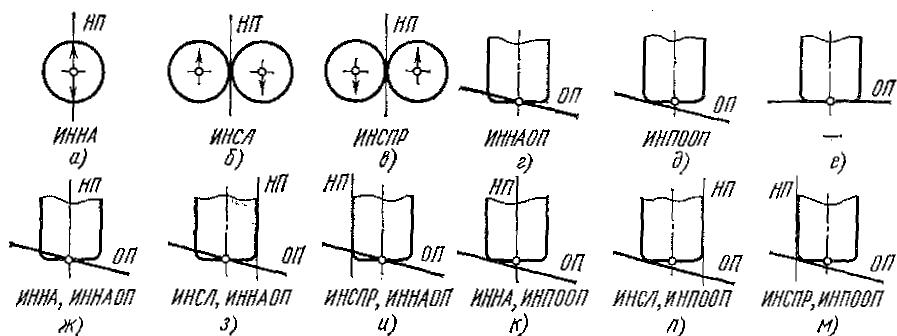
Положение инструмента относительно направляющей и обрабатываемой поверхностей
